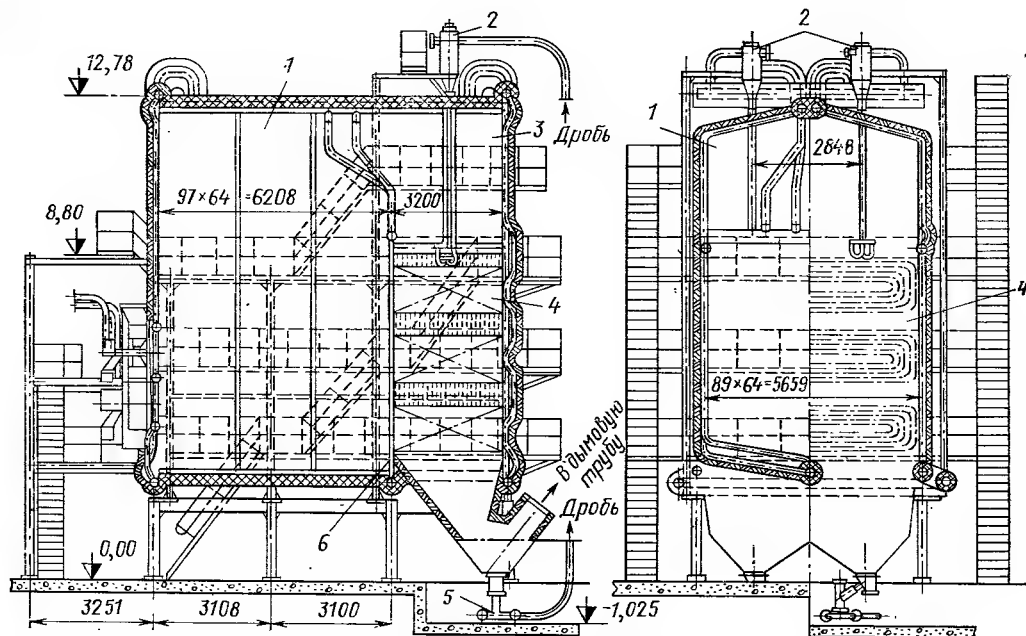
Общий вид пикового водогрейного котла KBGM-100 для работы на газе и мазуте с П-образной компоновкой поверхностей нагрева, оборудованного системой дробеочистки.
